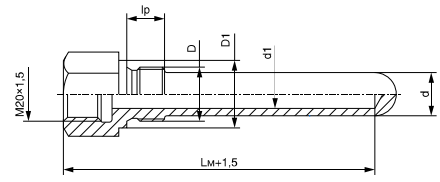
ГТ-712 цилиндрическая для ДТ с неподвижным штуцером
